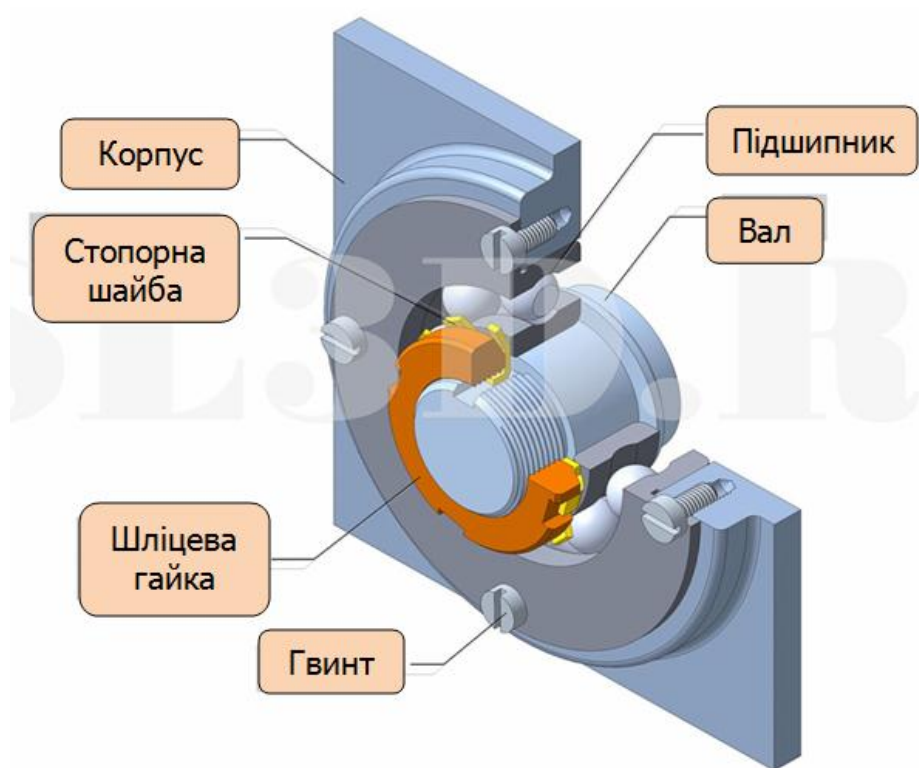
Кріплення підшипника з фланцем на зовнішній обоймі підшипника.
